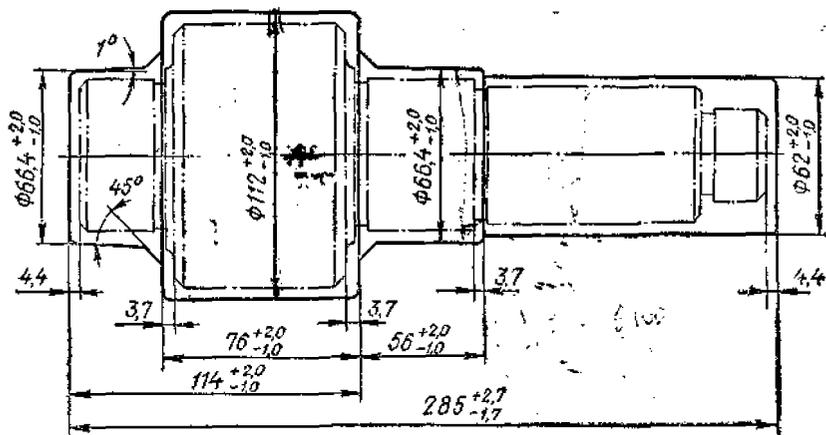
Заготовка шестерни ведущей (рис. 17) с начисленными припусками и допусками
